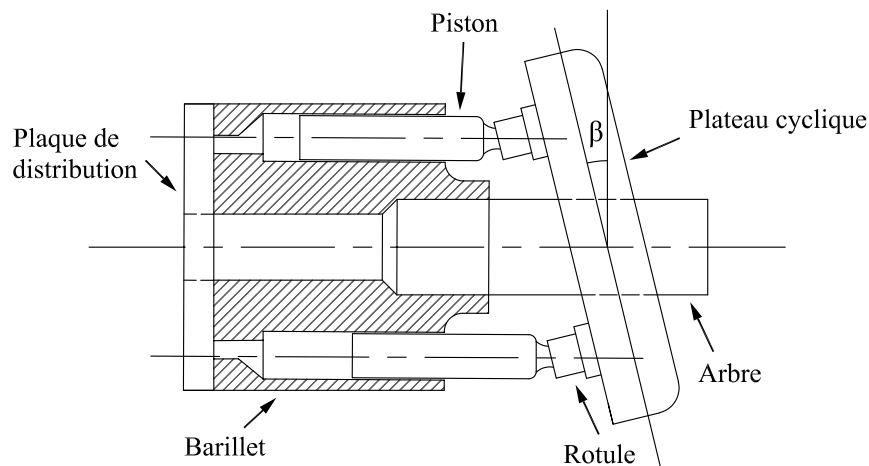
Coupe axiale d'une pompe à pistons axiaux, à barillet et à axe simple.
